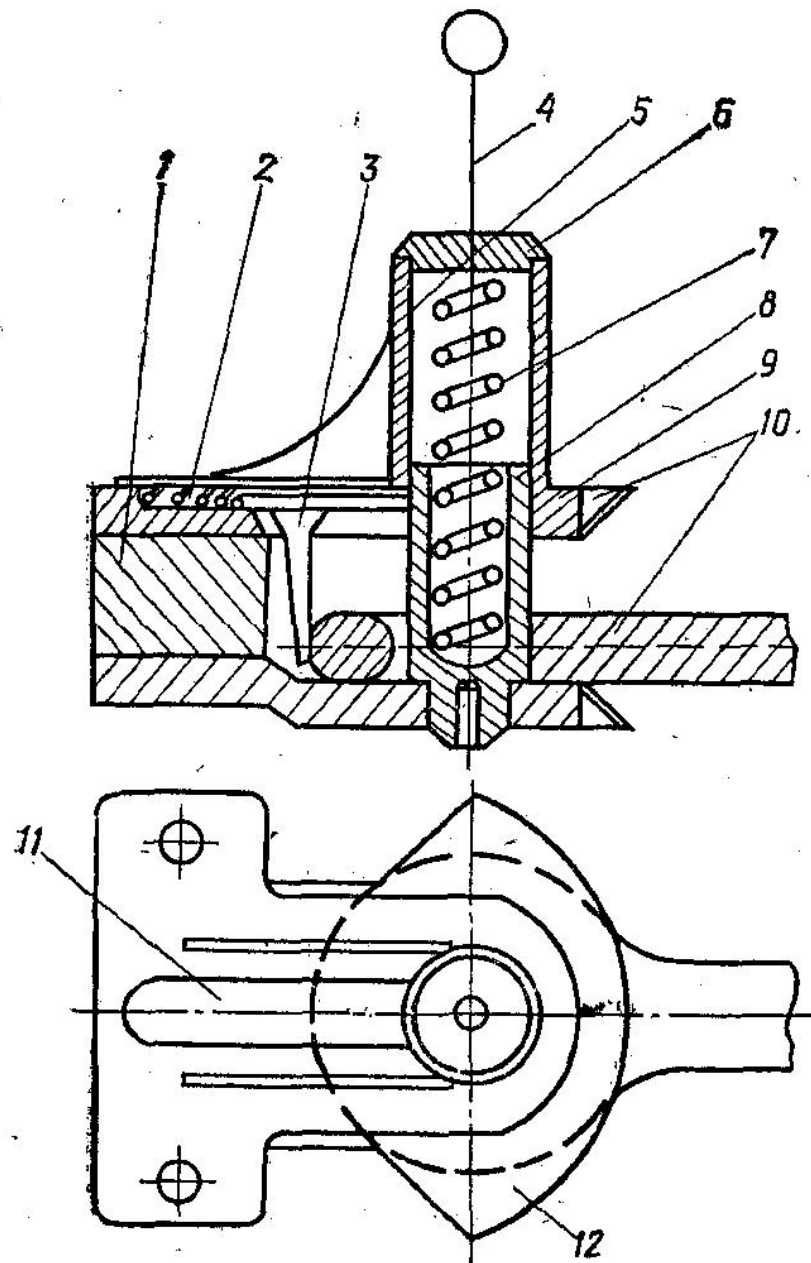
Конструкція автозчіпки для тракторів класу 3: 1 – поперечина; 2 і 7 – пружини; 3 – стопор; 4 – тросик; 5 – спрямівник; 6 – накривка; 8 – з'єднувальний палець; 9 – механізм з'єднання; 10 – корпус зчіпки; 11 – кришка; 12 – вловлювач
